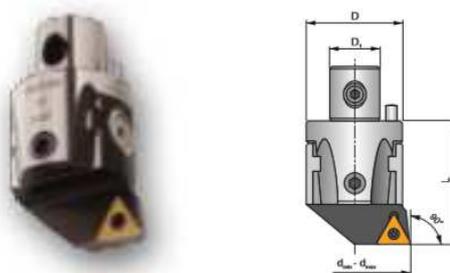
Расточная головка для чистовой обработки ф. Pramet
